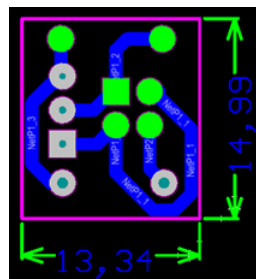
Ruteado y dimensiones de la placa del sensor.
